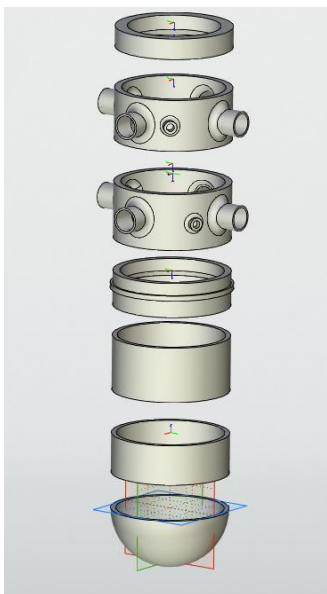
Обечайки корпуса реактора ВВЭР-1000
